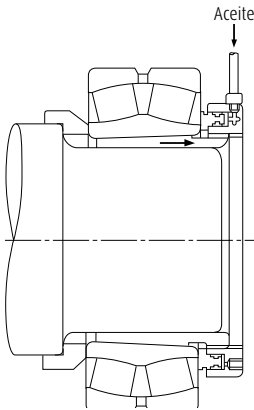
Desmontaje utilizando una Tuerca Hidráulica
